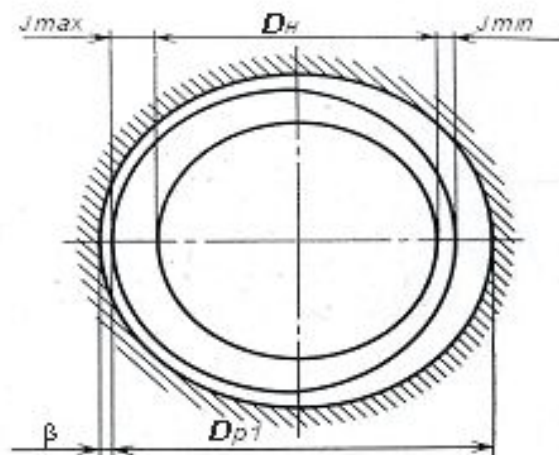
Порядок определения ремонтных размеров для отверстий и вала.
